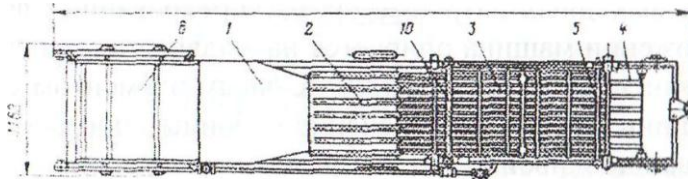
Схема установки для сортировки живой рыбы УРС-3: 1,2- ориентирующий и направляющий лотки; 3, 4 - пакеты труб; 5 устройство для регулирования угла наклона верхнего направляющего пакета по отношению к нижнему; 6 - сифонное устройство; 7 - рама; 8 - колесо; 9 - винтовой упор; 10 душирующее устройство; 11 - отводящий лоток
